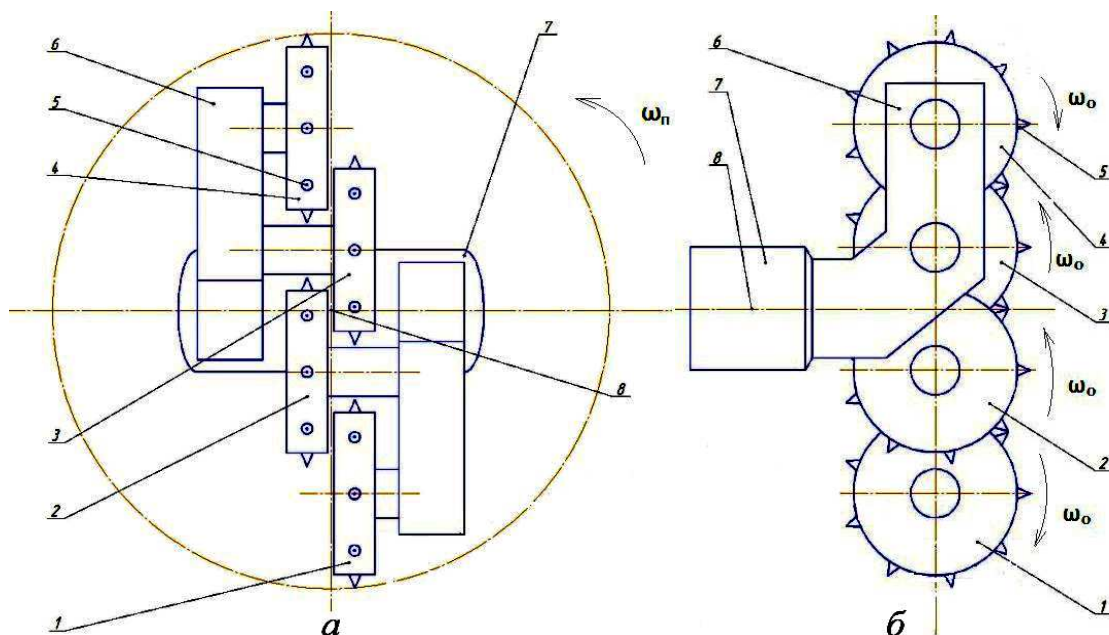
Схема исполнительного органа: а – вид спереди; б – вид сбоку
